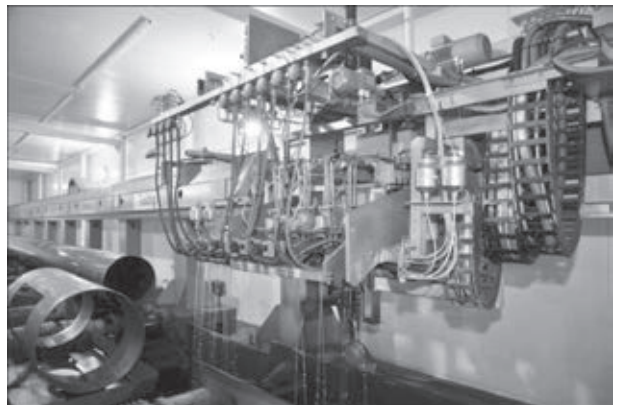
Установка для ультразвукового контроля основного металла и сварного соединения трубы
